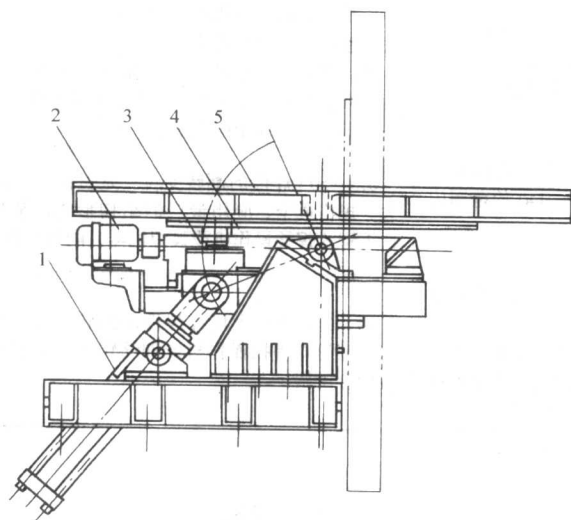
工作台倾斜采用液压缸推动的焊接变位机
